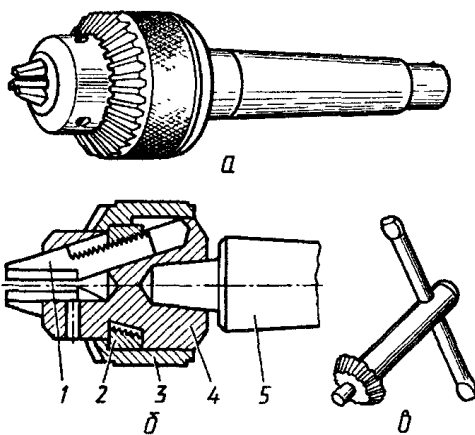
Патрон для закріплення свердла: а - загальний вигляд; б - розріз: 1 - кулачок; 2 - кільце (гайка) з різьбою; 3 - обойма; 4 - корпус; 5 - хвостовик; в - ключ
